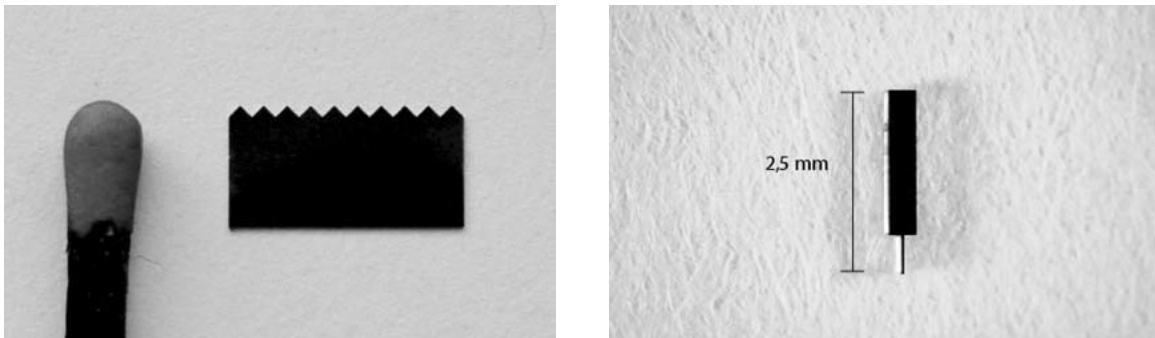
Mikrosystemtechnisch hergestellte Diamantkammwerkzeuge [2]
